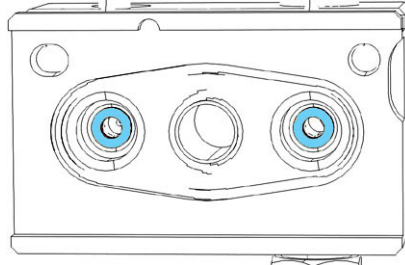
Pumpenkopf mit installierten Kolbendichtungen und Stützringen
